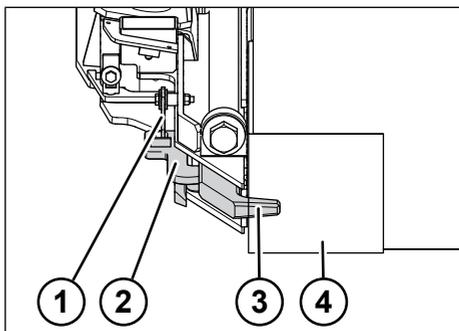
Meccanismo di presa container in posizione di riposo
